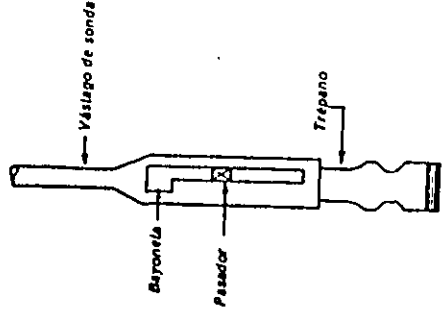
Trépano de caída libre dispositivo de bavo-neta
